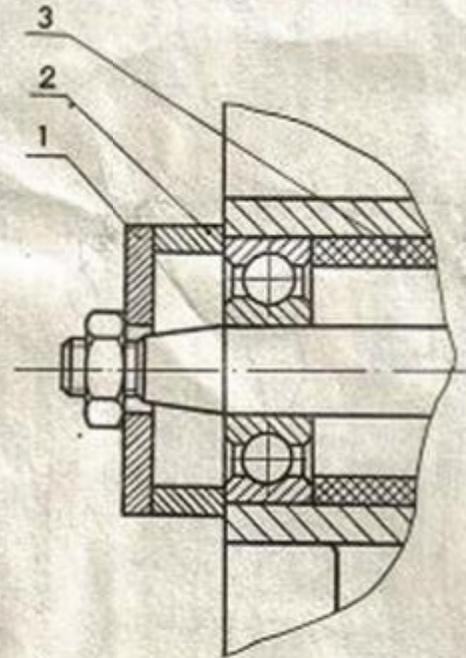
Допрессовка коленчатого вала в левую половину картера:
